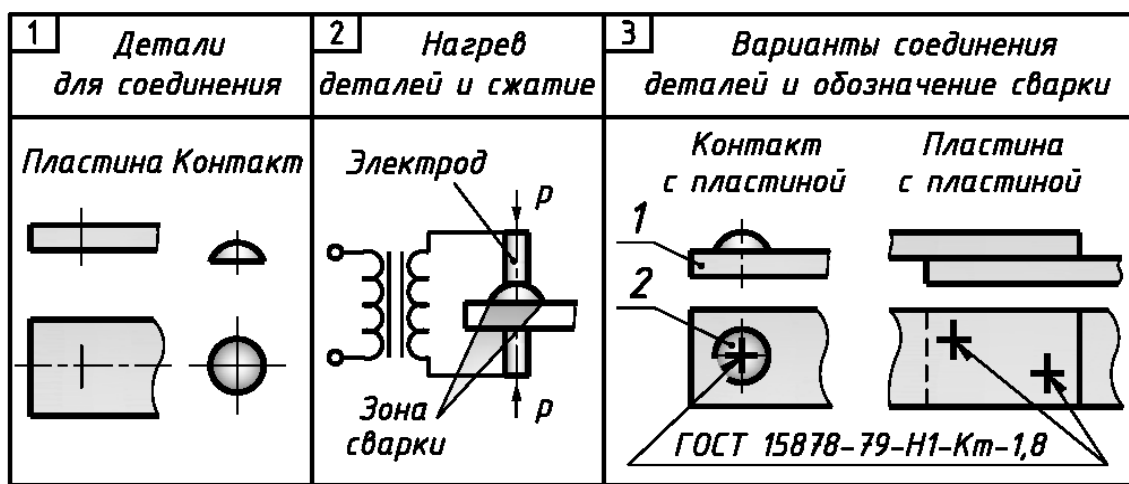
Основные этапы создания неразъемного соединения операцией «Контактная точечная сварка» и варианты соединения деталей
